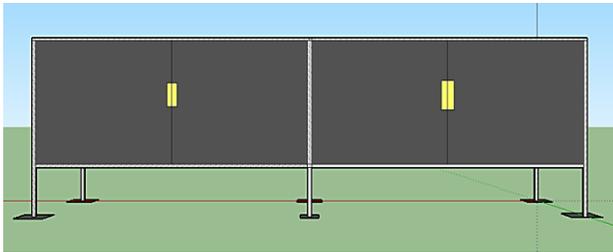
Estructura del DS en 3D, proyección posterior texturizado.
